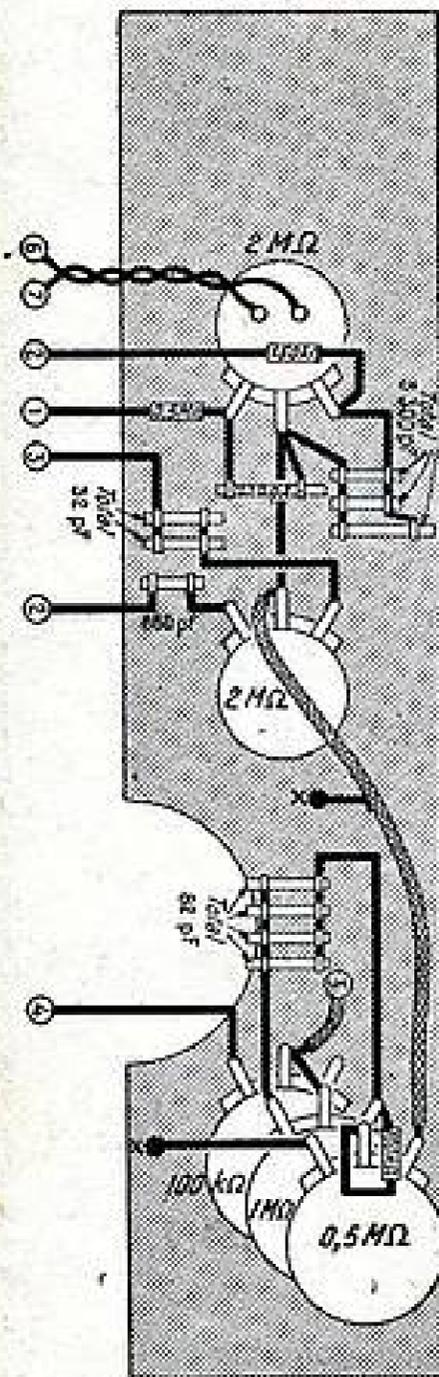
Plan de câblage de l'équerre supportant les potentiomètres.
